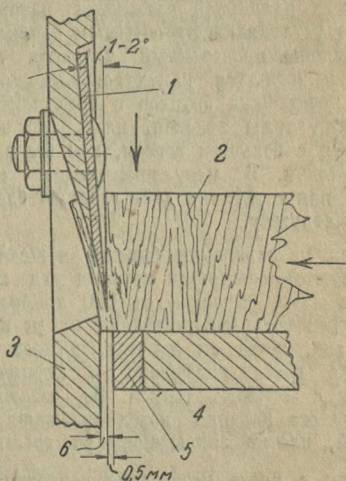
Схема установки ножа и подпора на дисковом станке:
